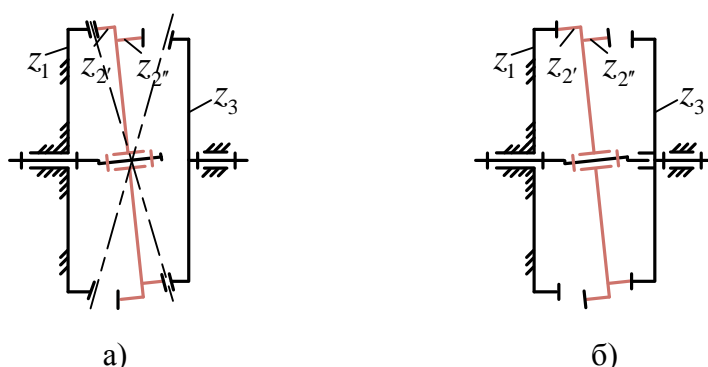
Планетарный редуктор с двухвенцовым прецессирующим сателлитом: а) с коническими зубьями; б) с торцевыми зубьями
